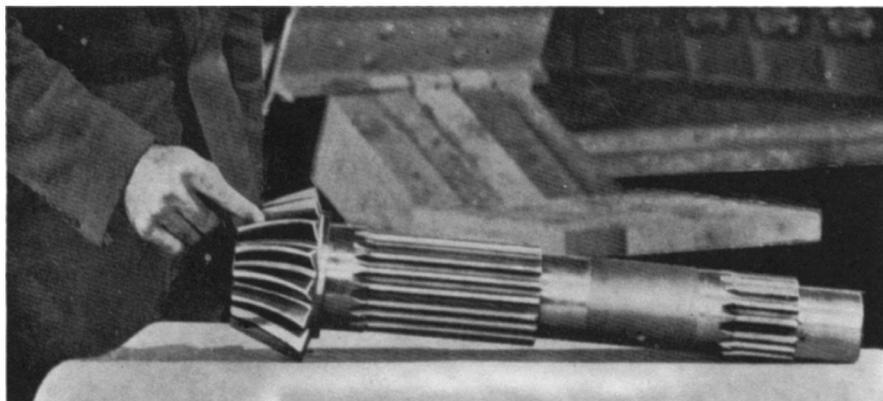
Pinhão motor terminado. Esta engrenagem deve ser usinada durante a produção e antes de ser usada, suas propriedades devem ser alteradas a fim de torná-la tenaz. (Cortesia de Climax Molybdenum Co.).
